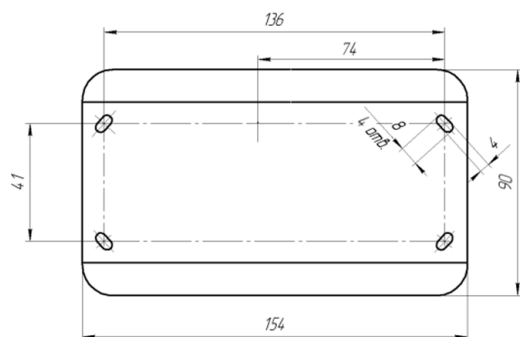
Розмітка отворів на основі корпусу оповіщувача
